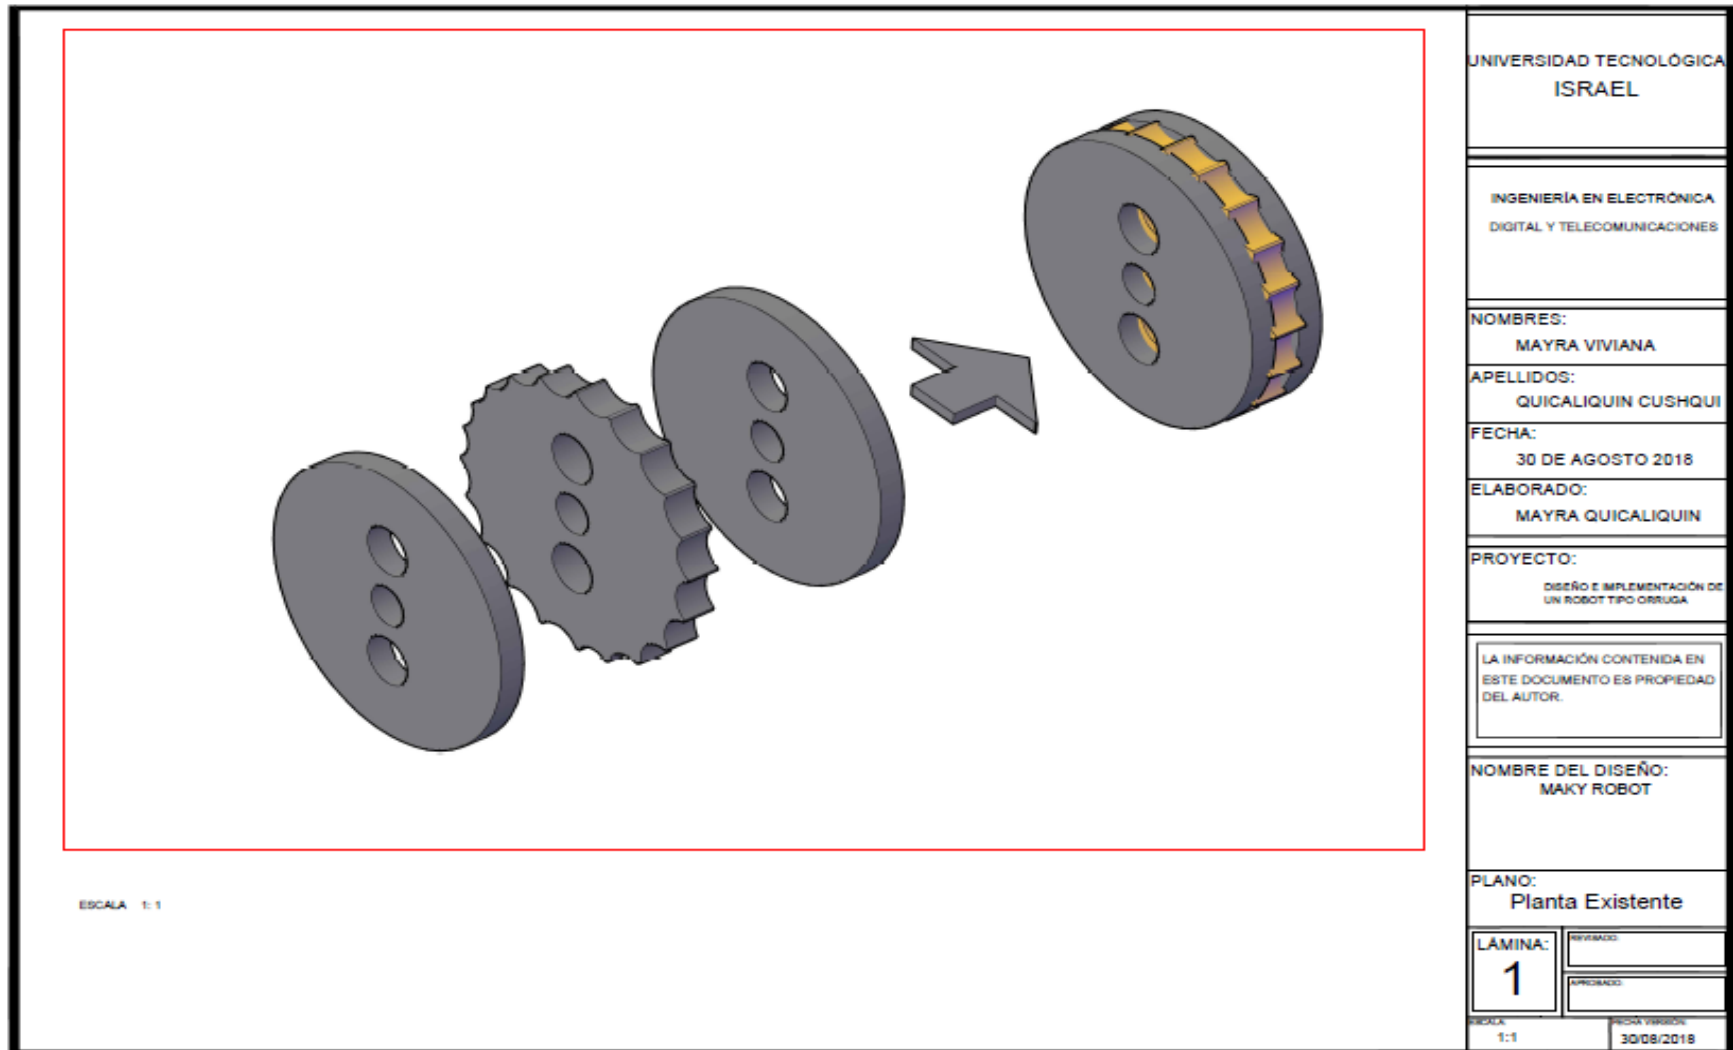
Ensamblaje rueda principal(engranaje)
